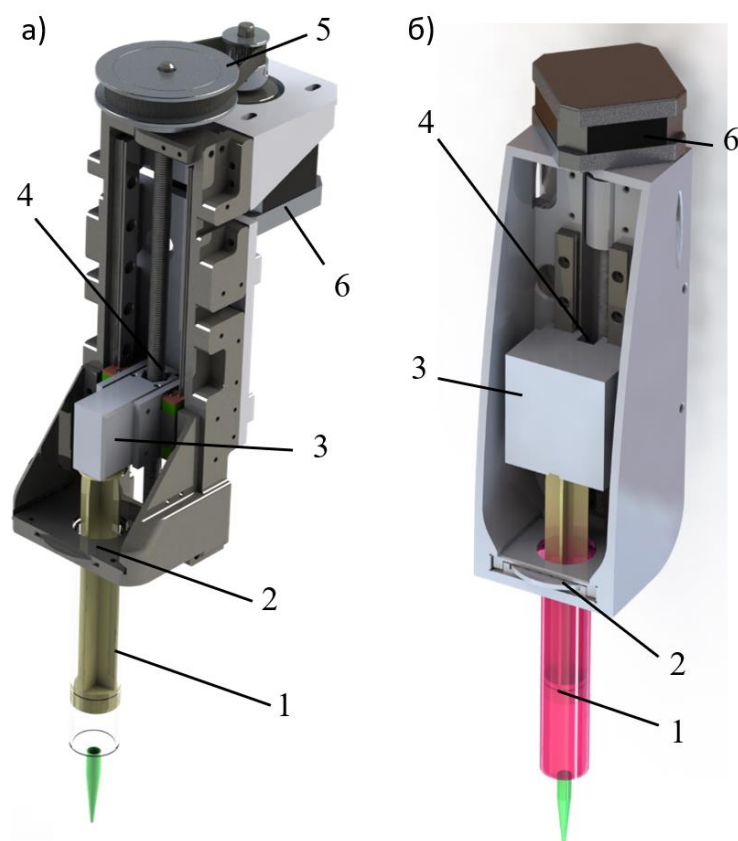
Мехатронный дозатор в двух исполнениях: 1 – шприц; 2 – крепление шприца; 3 – толкатель штока шприца; 4 – передача винт-гайка; 5 – ременная передача; 6 – шаговый двигатель
